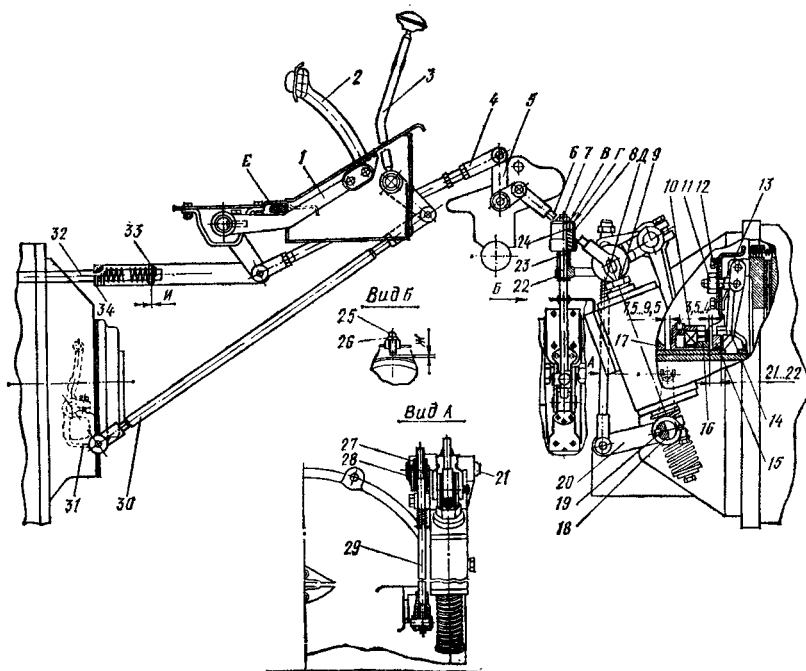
Регулировка механизма управления сцеплением и тормозком:
